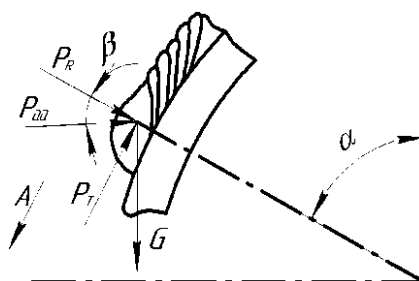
Схема сил действующих на сварочную ванну
